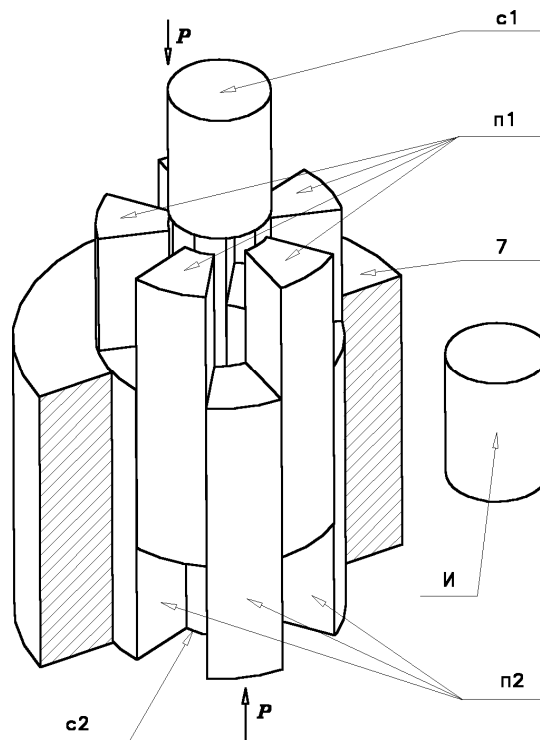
Пресс-форма для формования цилиндрической прессовки с десятью чередующимися, встречно-движущимися частями пассивной
